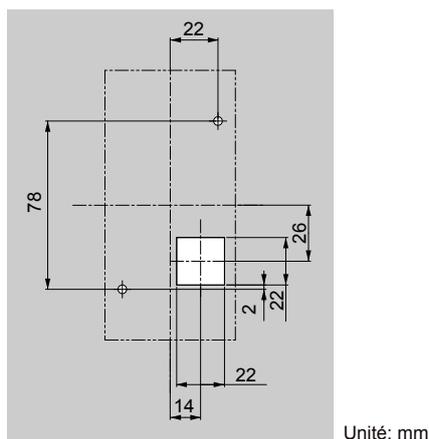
Dimensions de découpe du panneau (installation externe/vissage)
